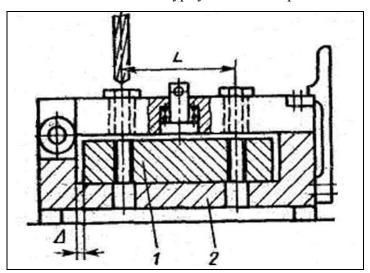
Пример установки заготовки по внешнему контуру
